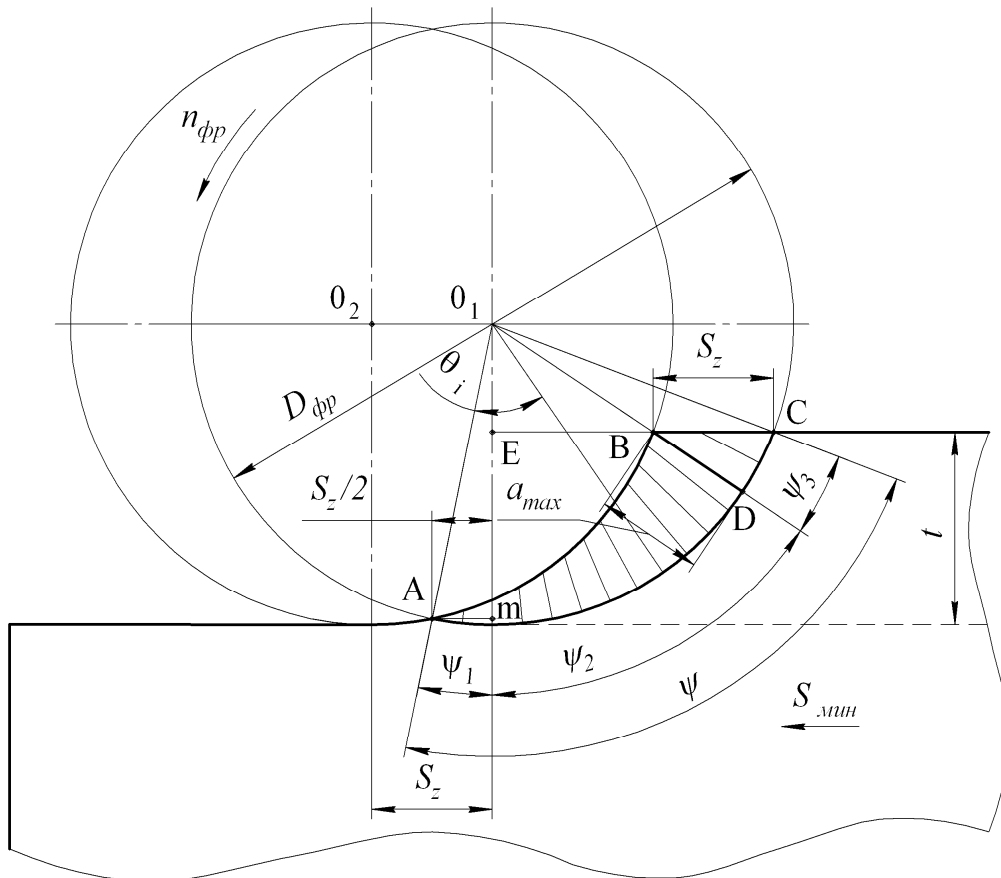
Схема сечения среза одним зубом фрезы при цилиндрическом фрезеровании (встречном)
